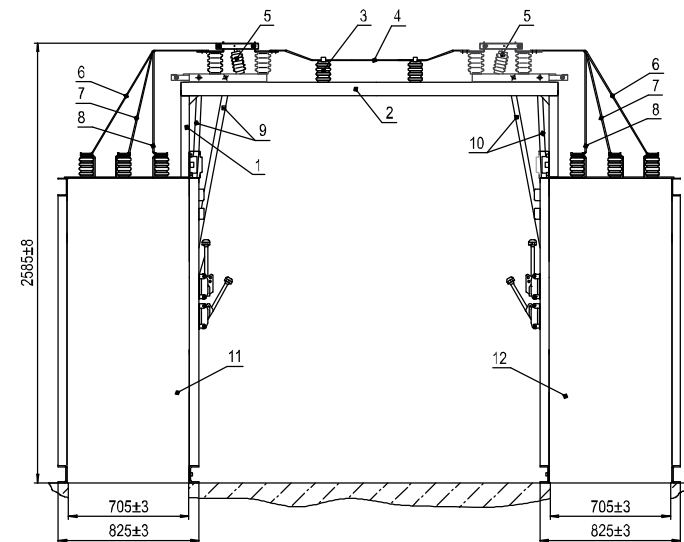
Габаритные, установочные, присоединительные размеры КСО-306 с установкой разъединителя на шинный мост:
